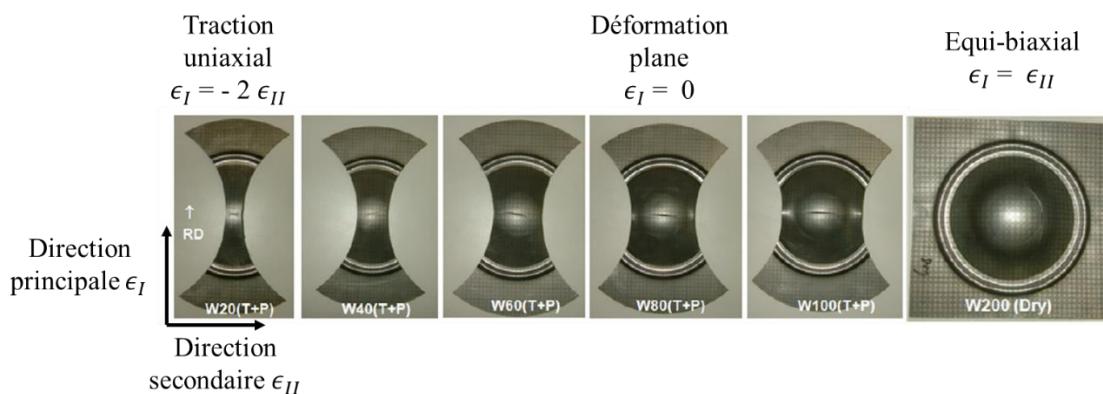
Formes déformées des éprouvettes de DP780 obtenues à partir d'essais d'emboutissage [34]
